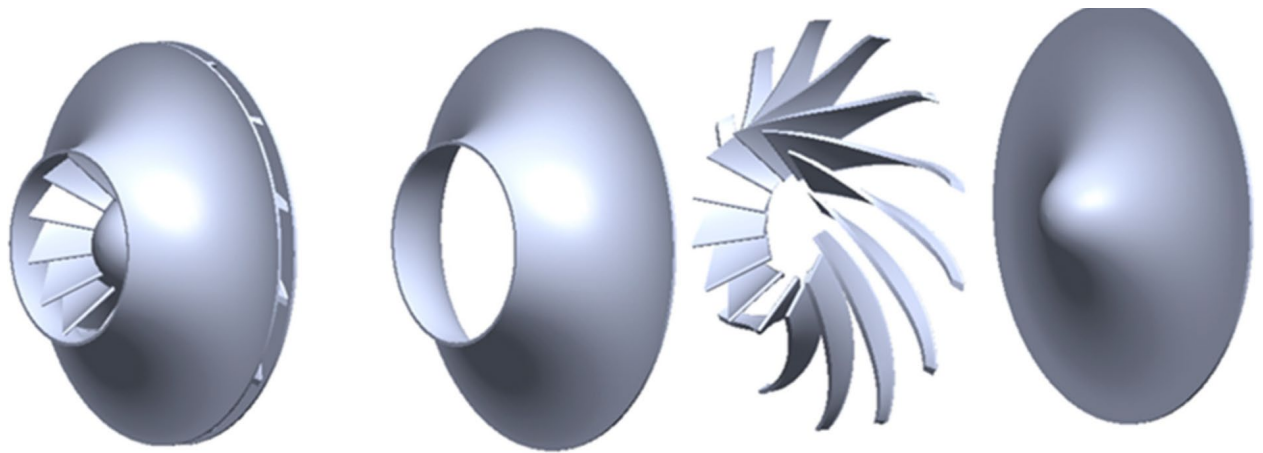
CAD-модель робочого колеса відцентрового компресора [18]
